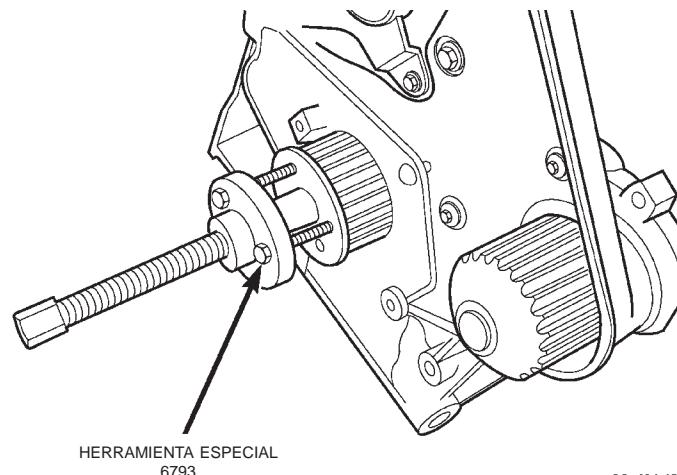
Rueda dentada del cigüeñal—Desmontaje
